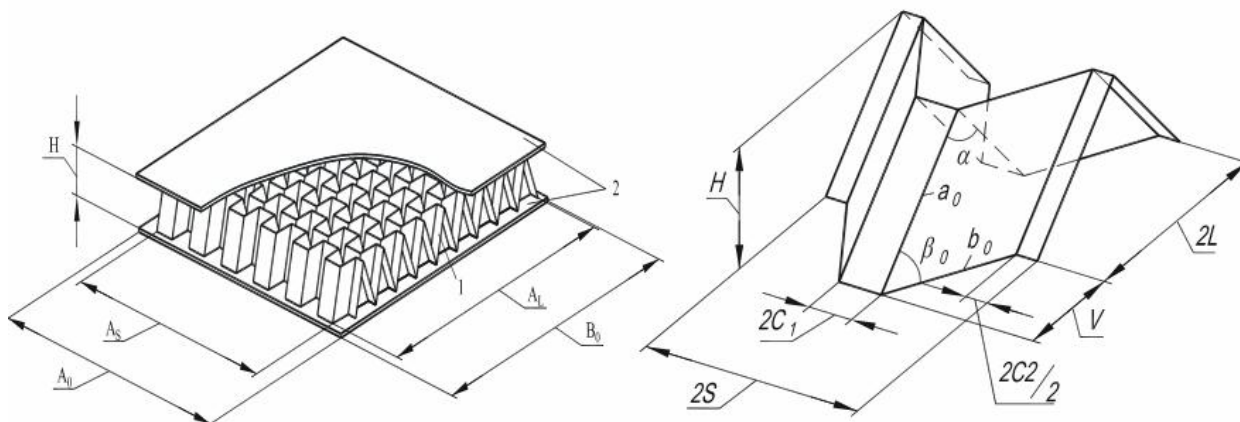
Испытываемый образец: 1 – заполнитель, 2 – обшивки
